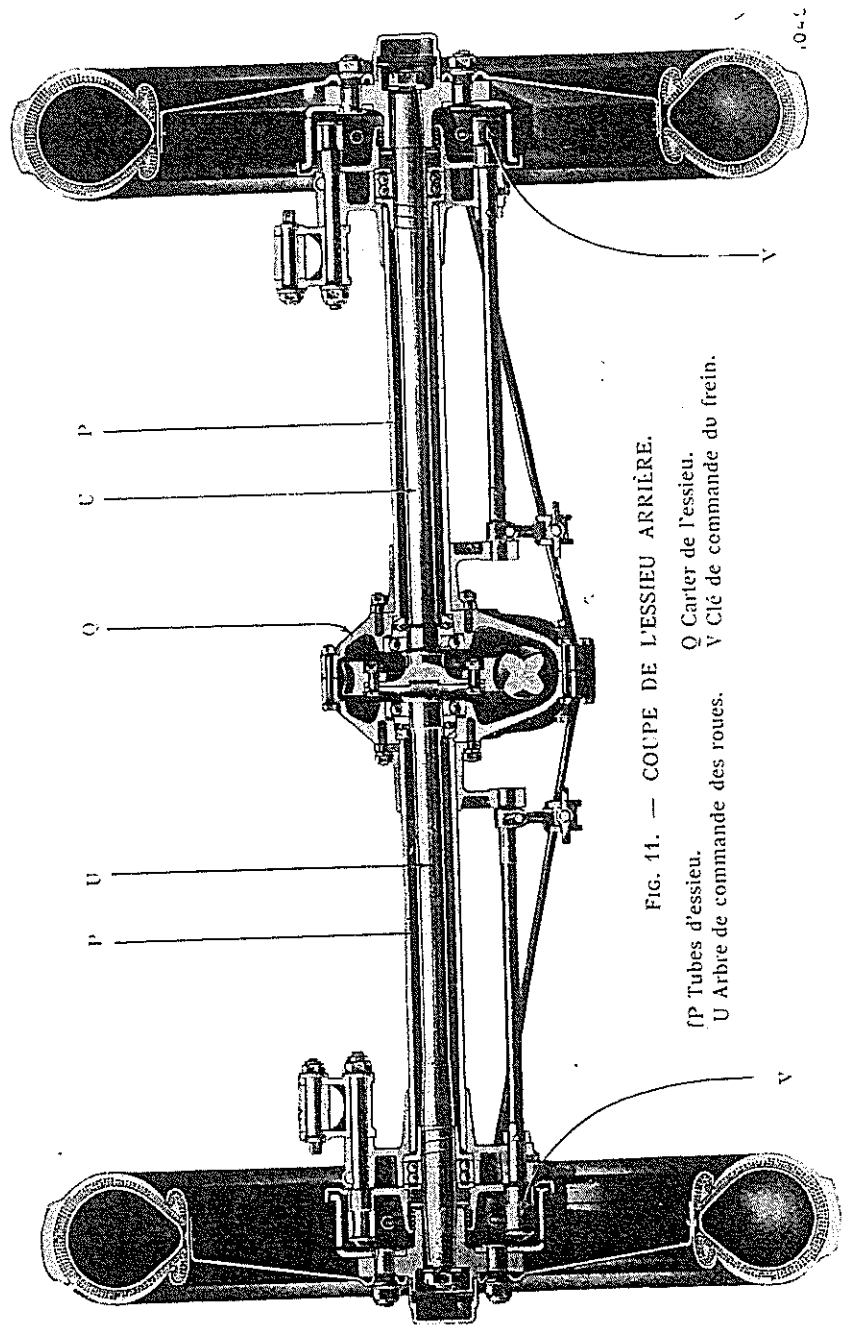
COUPE DE L'ESSIEU ARRIÈRE.
